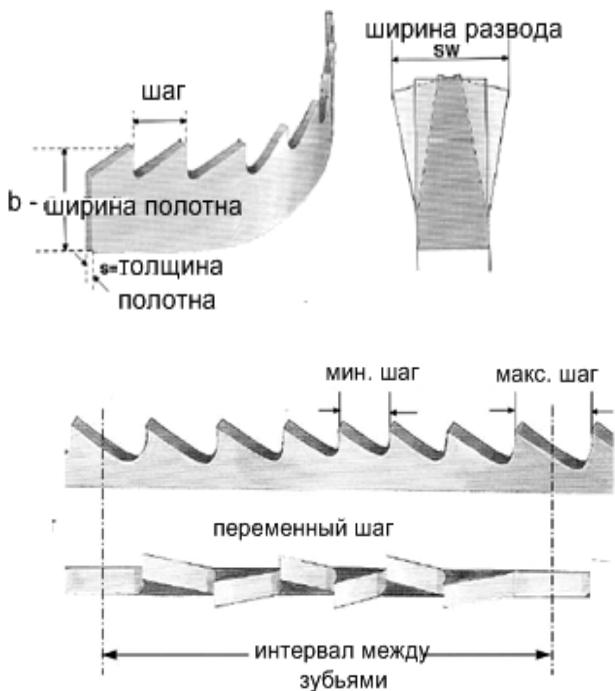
Схема основных параметров пил: толщина полотна; ширина полотна; вид и ширина разводки; шаг и тип разводки
